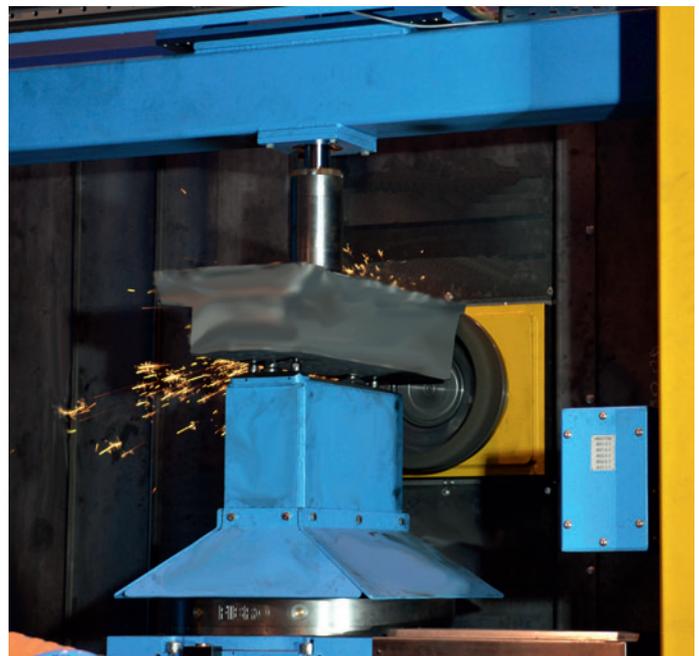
Schleifmaschine beim Bearbeitungsvorgang
